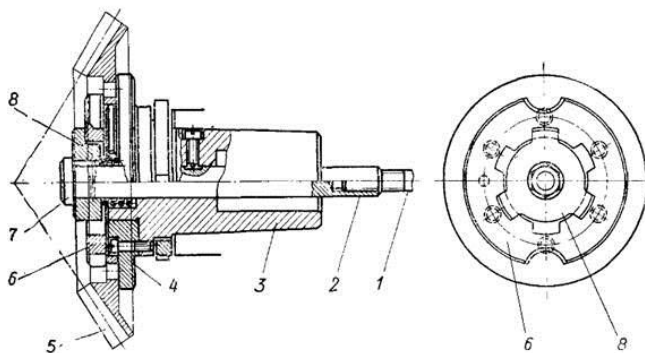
Пристосування з пневмоприводом для нарізання зубів кінцевого колеса на зубонарізному верстаті
